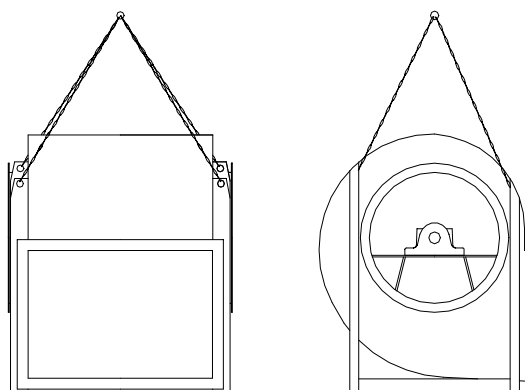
Ejemplo de levantamiento de los ventiladores centrífugos de aspiración doble
